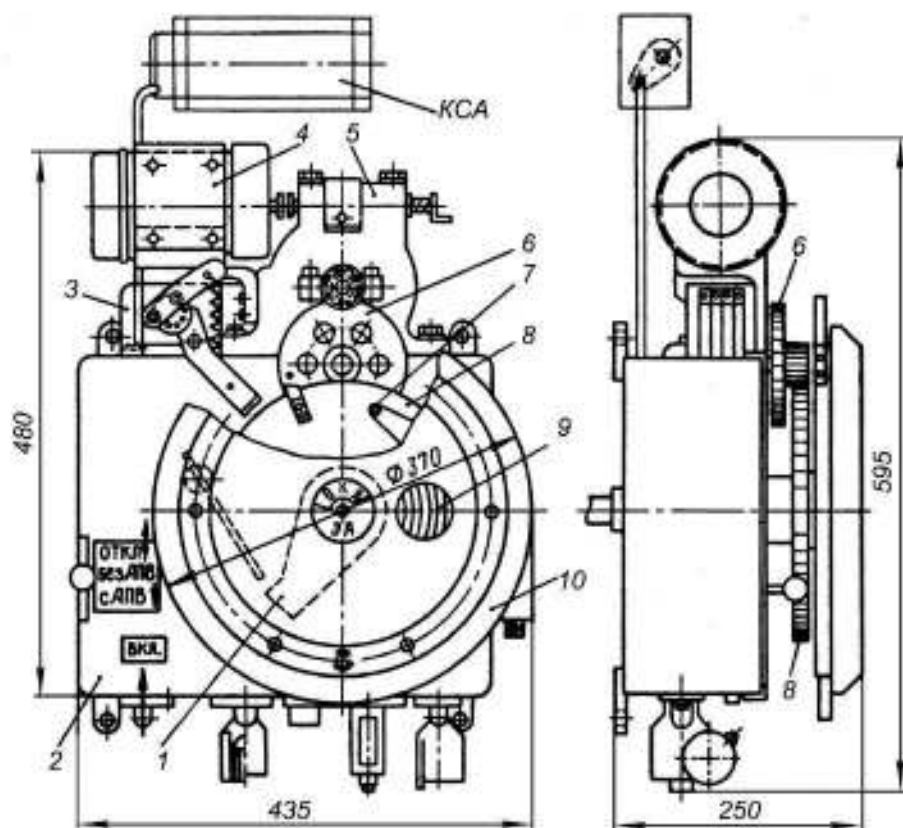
Пружинный привод см моторным редуктором ППМ-10: 1 – заводной рычаг; 2 – корпус; 3 – конечный выключатель; 4 – электродвигатель; 5 – редуктор; 6 – большая шестерня зубчатой передачи; 7 – ролик ведущей собачки; 8 – шестерня развода; 9 – спиральная пружина; 10 – штурвал
